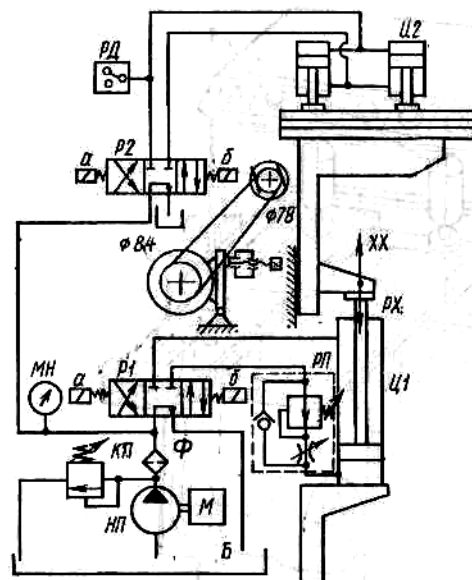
Гидрокинематическая схема одностороннего шипорезного станка для ящичных шипов ШПК-40:
